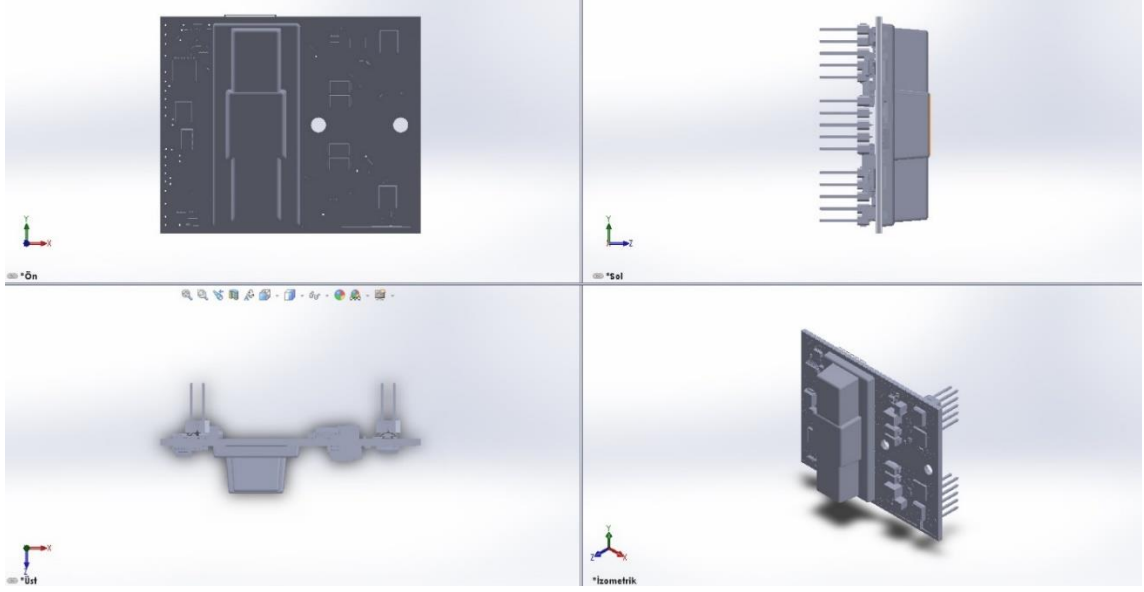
Adaptor Board 93 GD SKYPER® 42 LJ R ve montaj pin şeması
